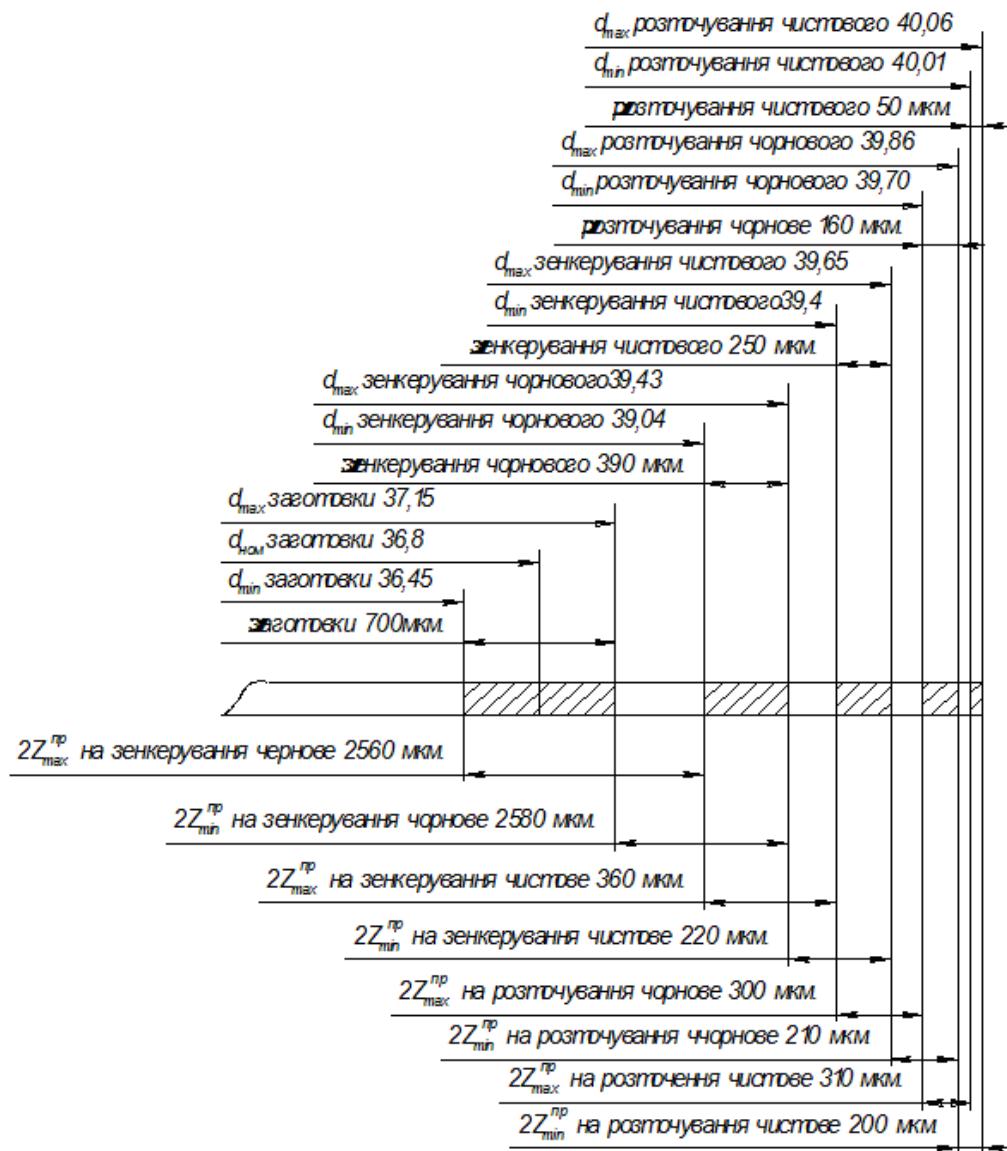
Схема розташування допусків і припусків
